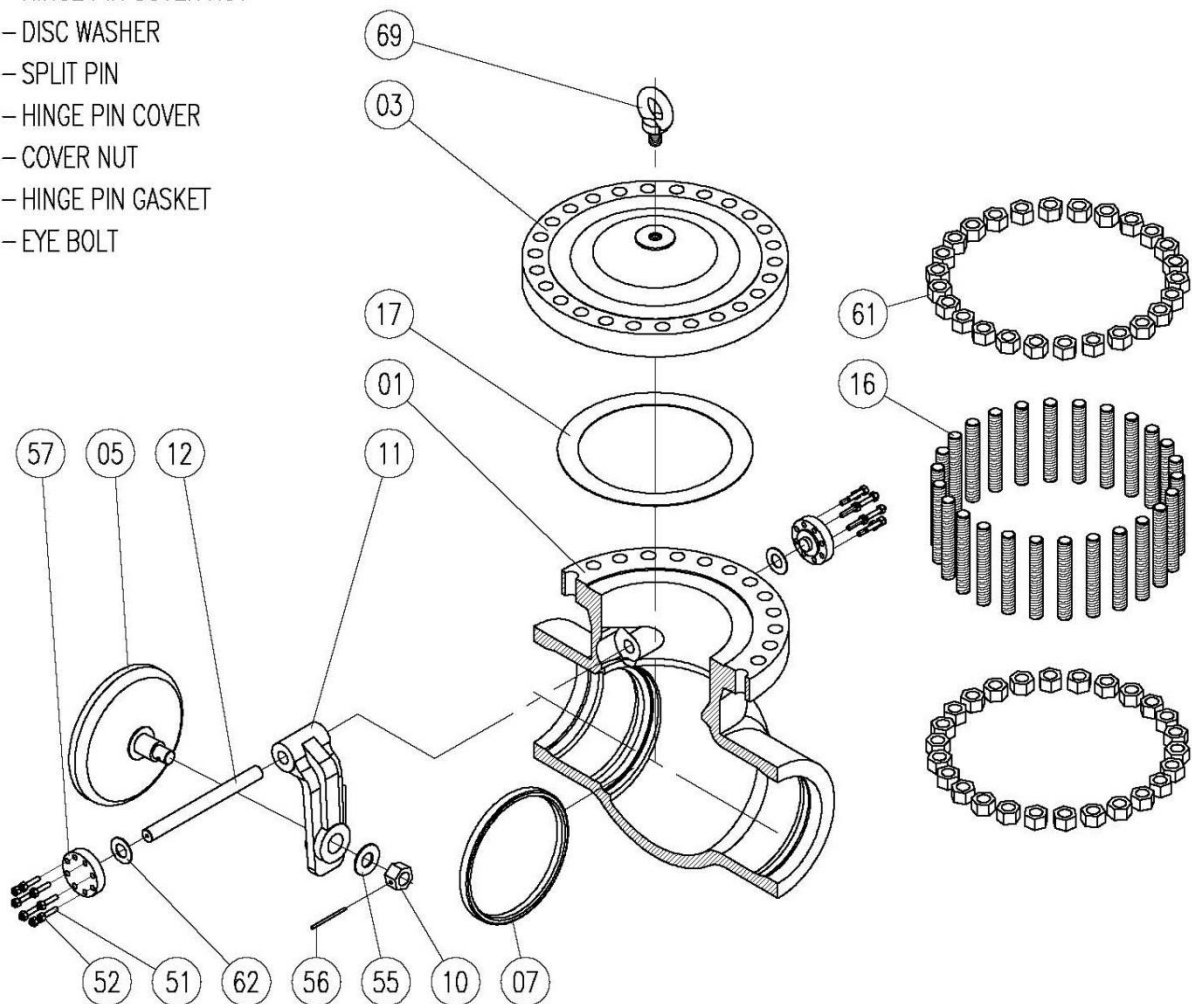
BOLTED COVER SWING CHECK 밸브 분해도
